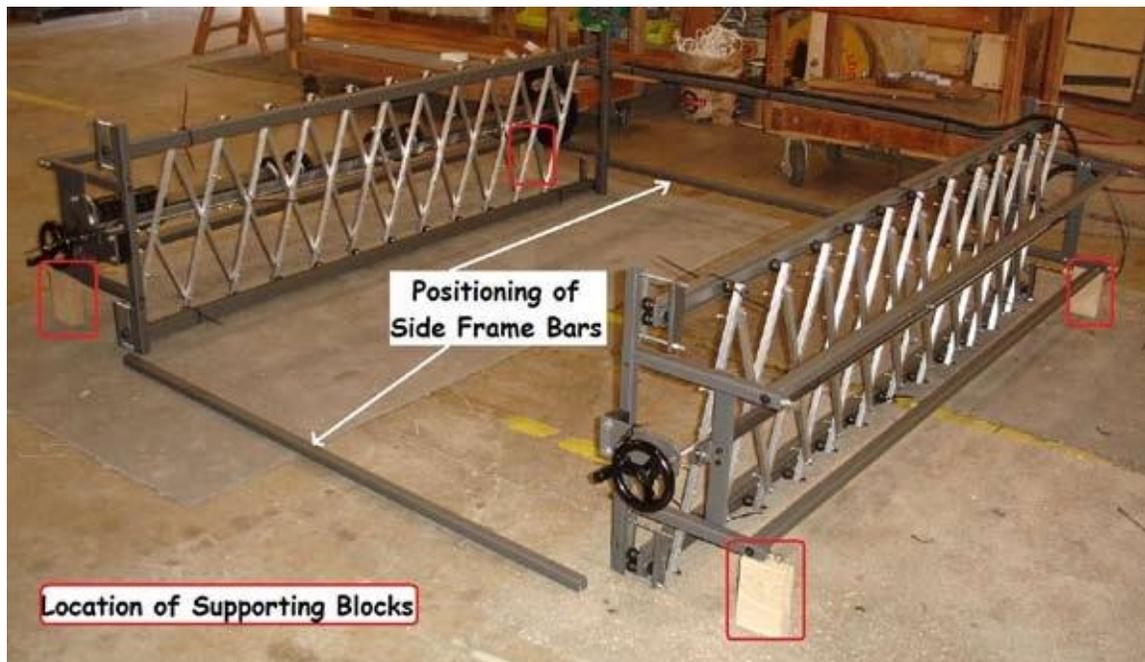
Disposition des pièces du cadre de module pour l'assemblage
